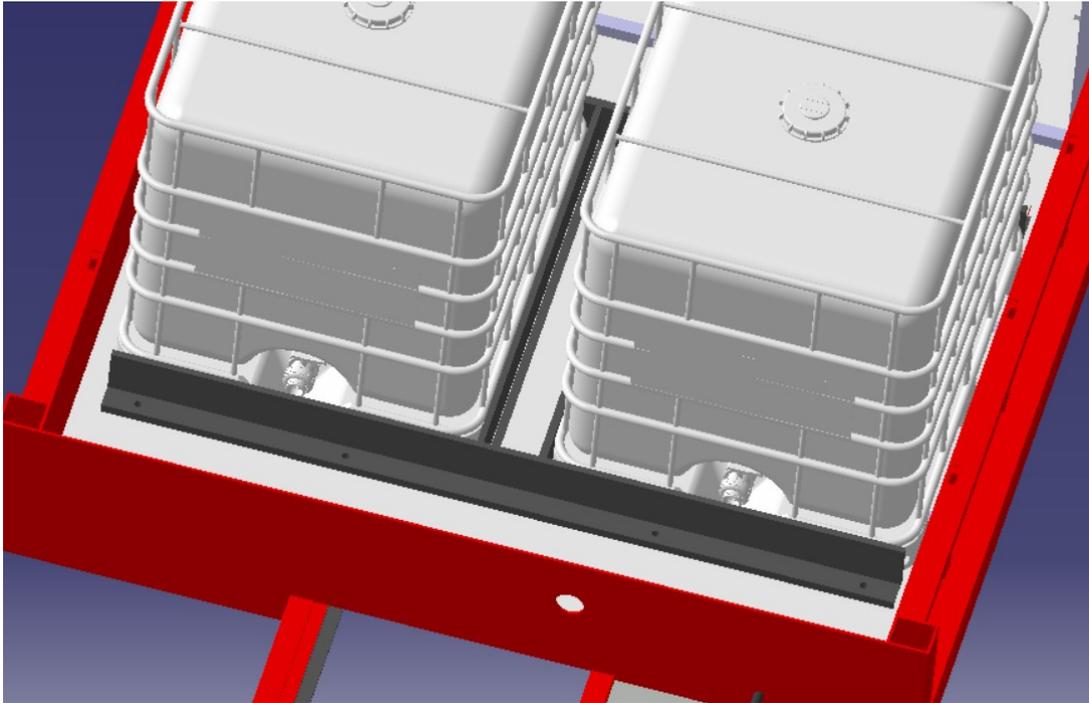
Cantoneiras laminadas para contenção dos tanques.
